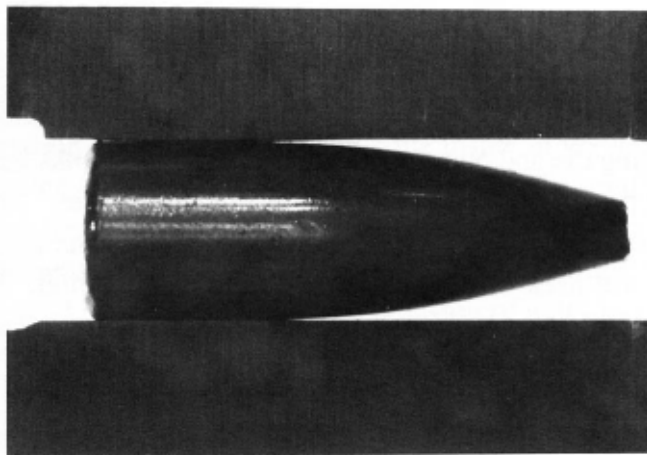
Фотография 90-грановой пули HP калибра 270, обжатой с 0,2770 до 0,2765 дюйма в диаметре, находящейся между параллельными губками штангенциркуля. Сравнение с Рисунком 7-6 показывает, насколько обжимка пули увеличивает длину цилиндрической части хвостовика.
